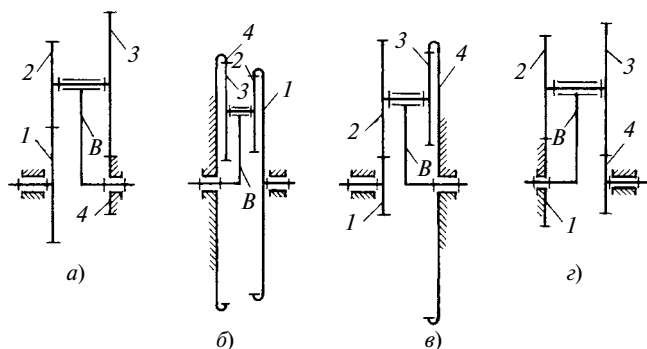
Типовые схемы планетарных механизмов с двумя центральными зубчатыми колесами и сдвоенным сателлитом
